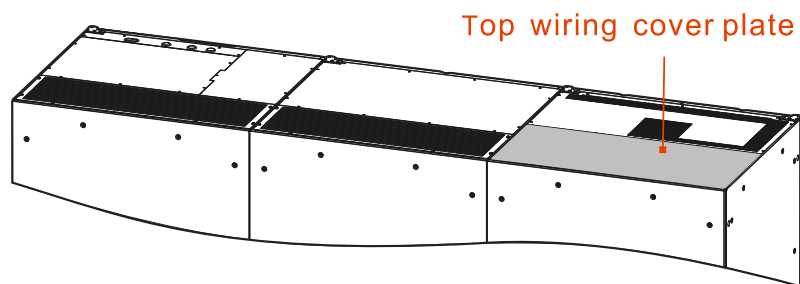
Расположение верхней крышки KR331000, KR331200, закрывающей зону электрических подсоединений
